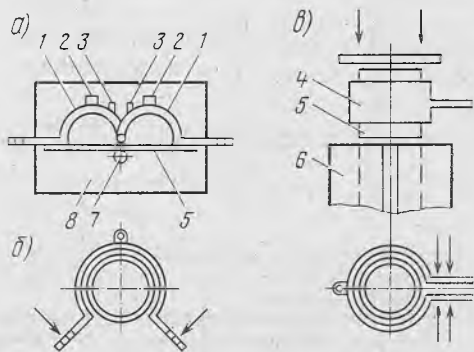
Захват для предварительного свертывания пластин и ввода их в пресс-форму:
